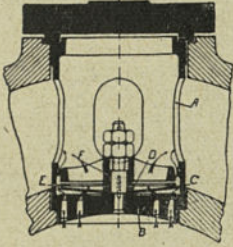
Coupe d'une soupape à disque d'un compresseur Sulzer.
